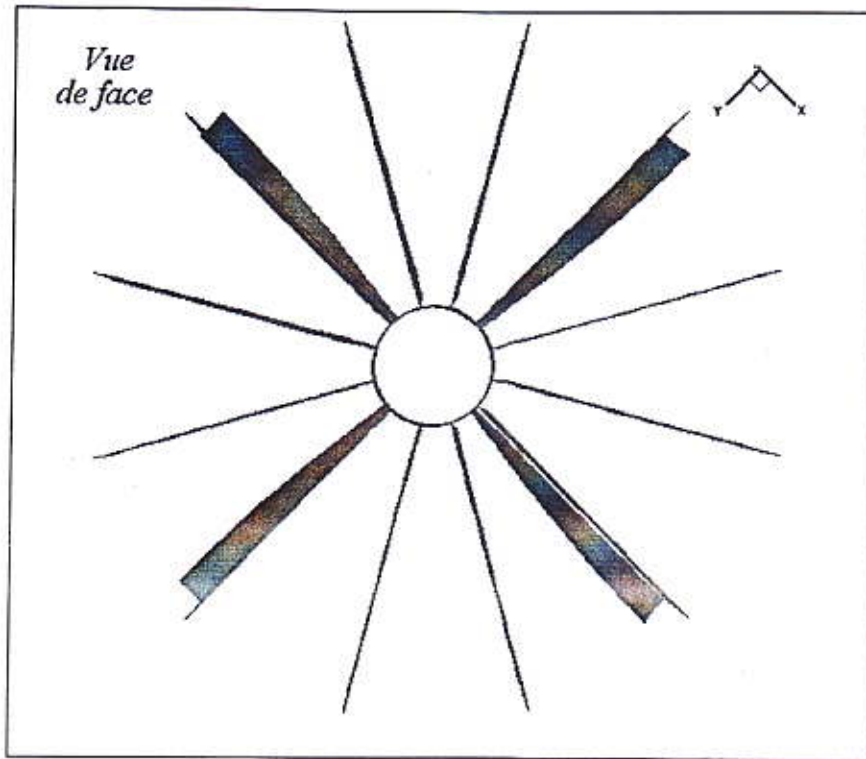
Vue de face des aubes de stator et de rotor
